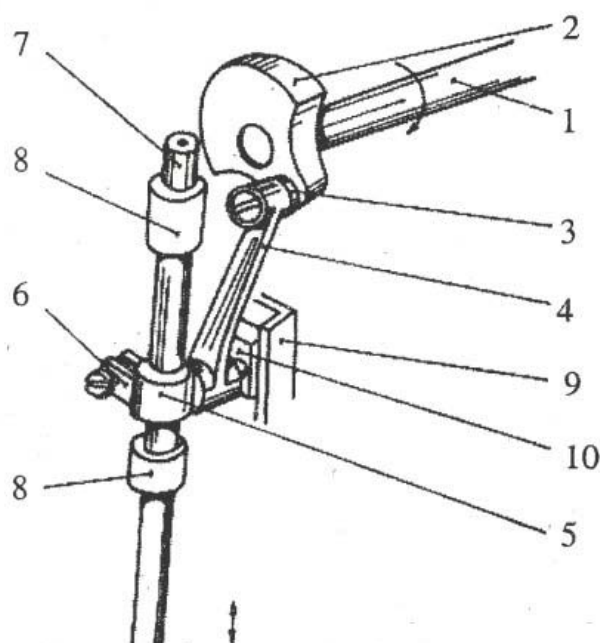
Mechanismus s dvouramennou pákou
